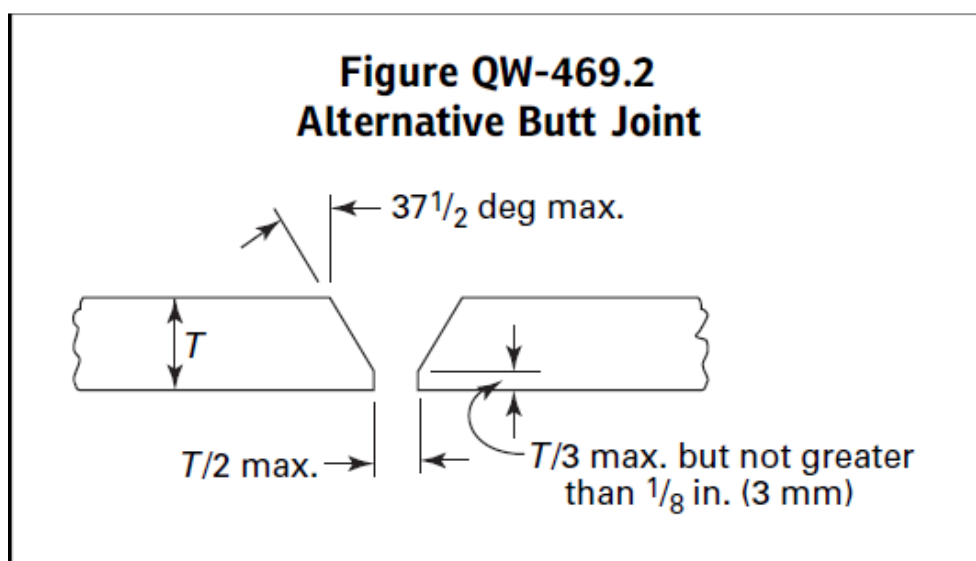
Dimensiones que debe tener una probeta de soldadura [2]
